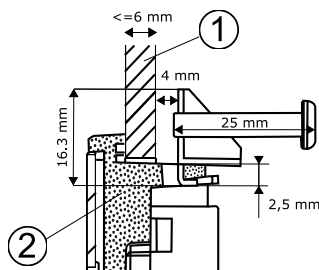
Dimensions du boîtier, vue latérale gauche
